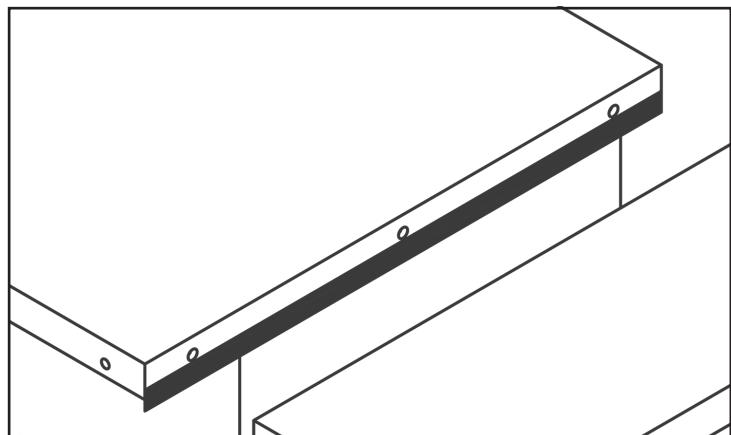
Colocación de cinta adhesiva para subir el ala.
